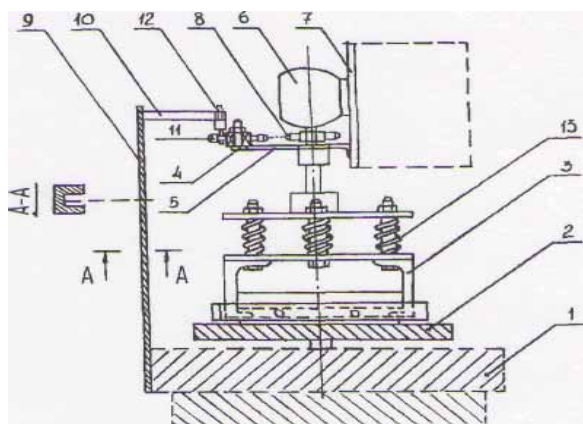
Схема доводочного станка: 1 – станина; 2 – притир; 3 – кассетница; 4 – эксцентрик; 5 – крепление эксцентрика; 6 – мотор-редуктор; 7 – подвижная опора; 8 – ведущая звёздочка цепной передачи; 9 – неподвижная опора; 10 – шатун; 11 – ведомая звёздочка цепной передачи; 12 – палец крепления шатуна с эксцентриком; 13 – компенсирующий механизм
